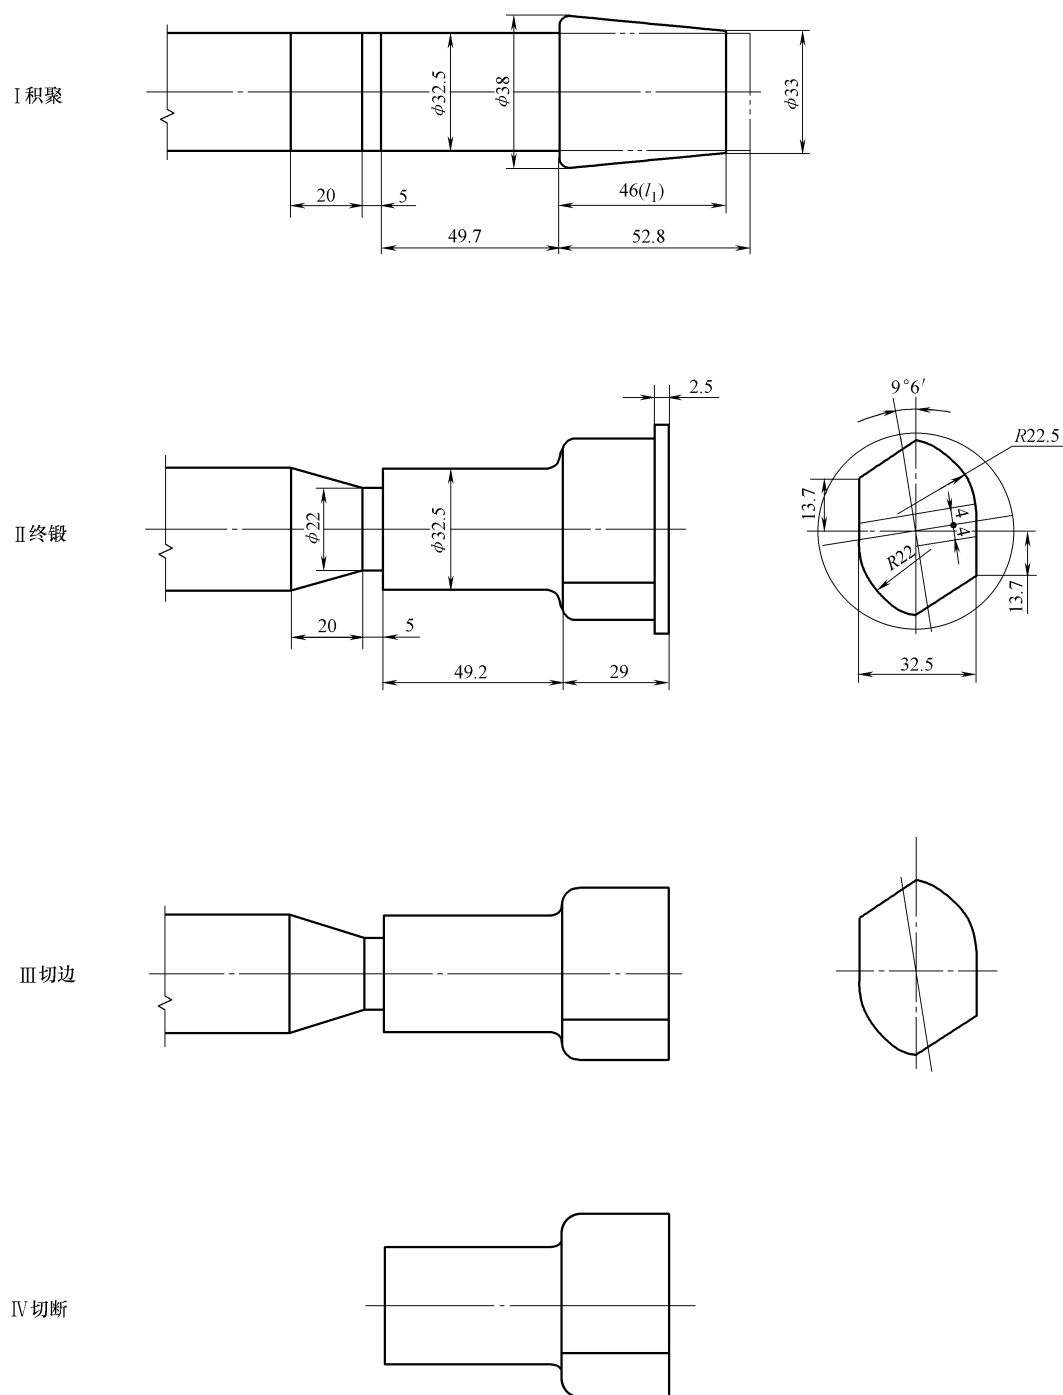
手制动齿轮工步 (热尺寸, 未注圆角 R3)
